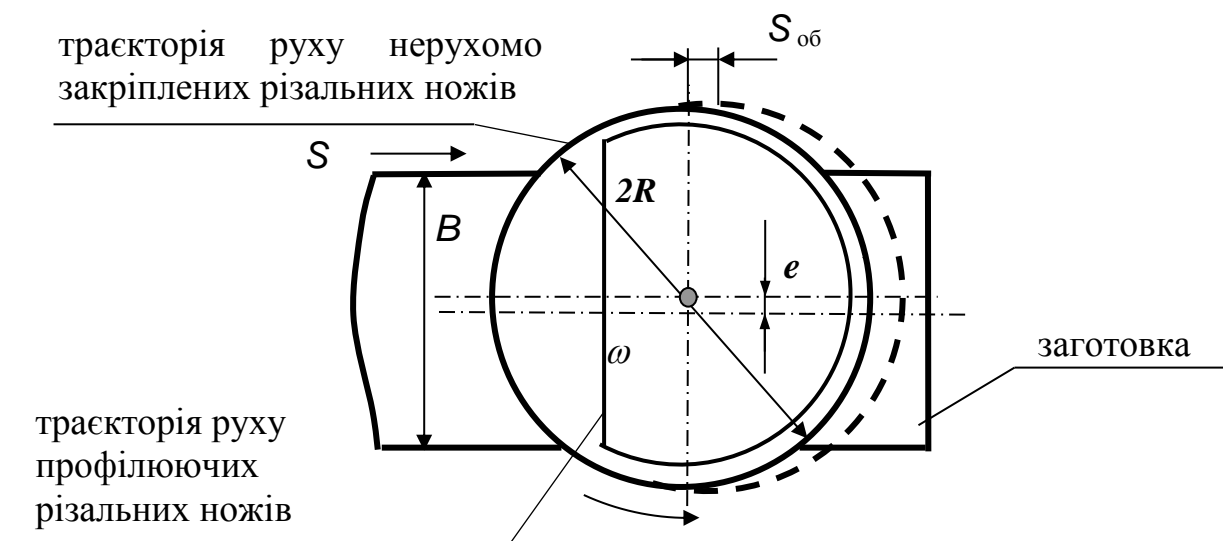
Запропоновані траєкторії руху різальних ножів торцевої фрези відносно заготовки
